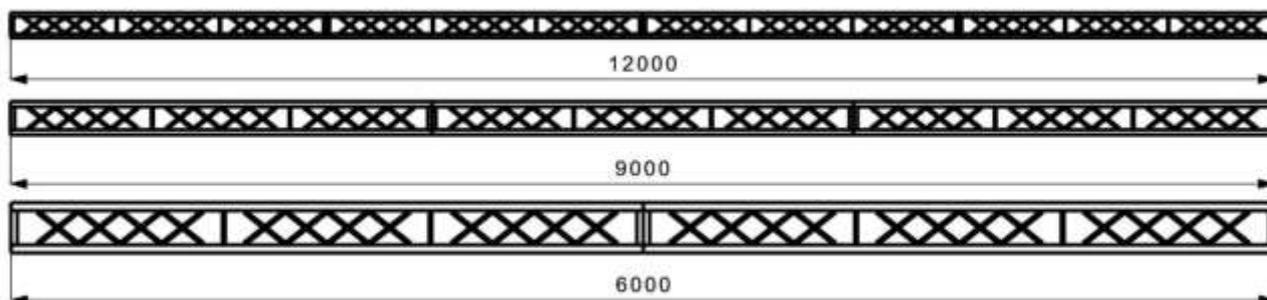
Desde arriba hacia abajo: viga de 12 m obtenida mediante la unión de 4 vigas TR333FE1-00-00; viga de 9 m obtenida mediante la unión de 3 vigas TR333FE1-00-00; viga de 6 m obtenida mediante la unión de 2 vigas TR333FE1-00-00.
